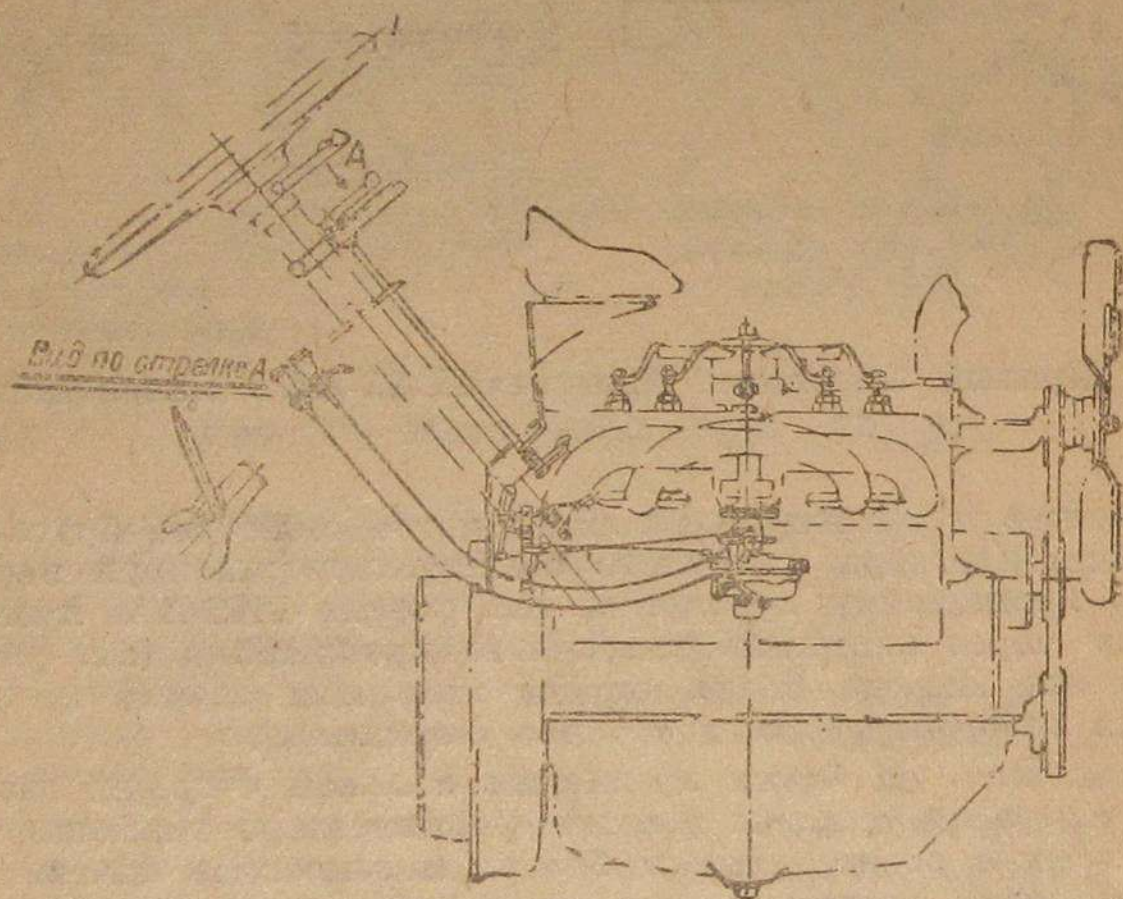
Управление смесителем и карбюратором двигателя (вид сбоку).
